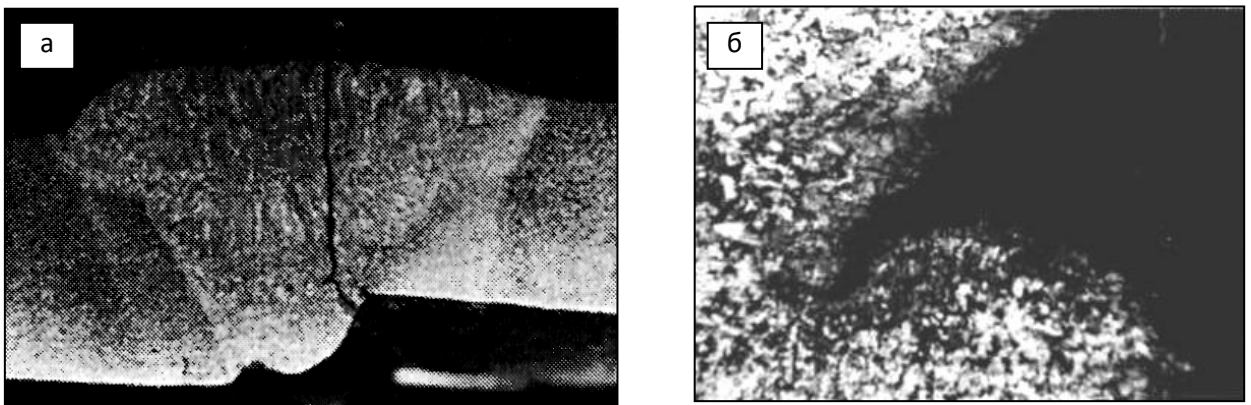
Трещина в сварном шве шлейфа скважины:
